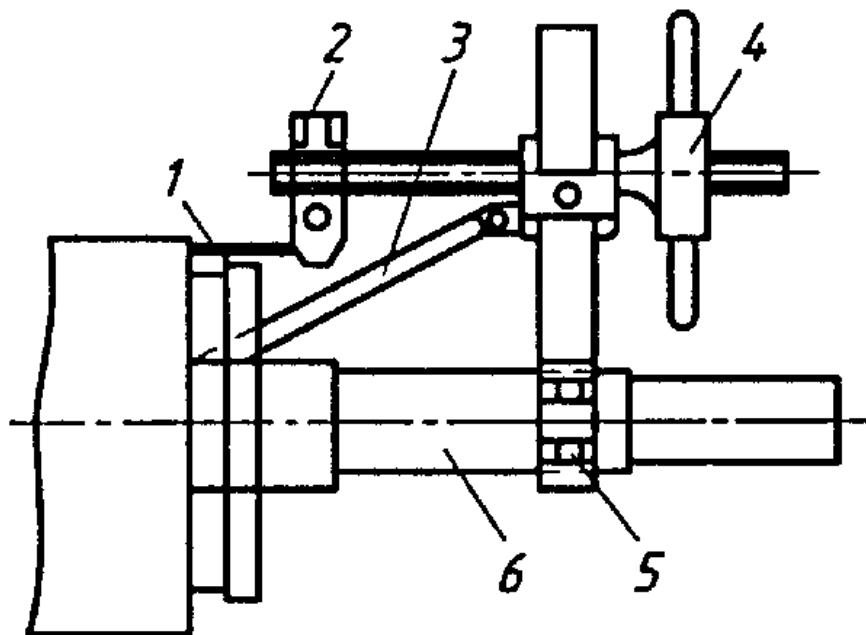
Приспособление для извлечения стержней из пазов ротора:
